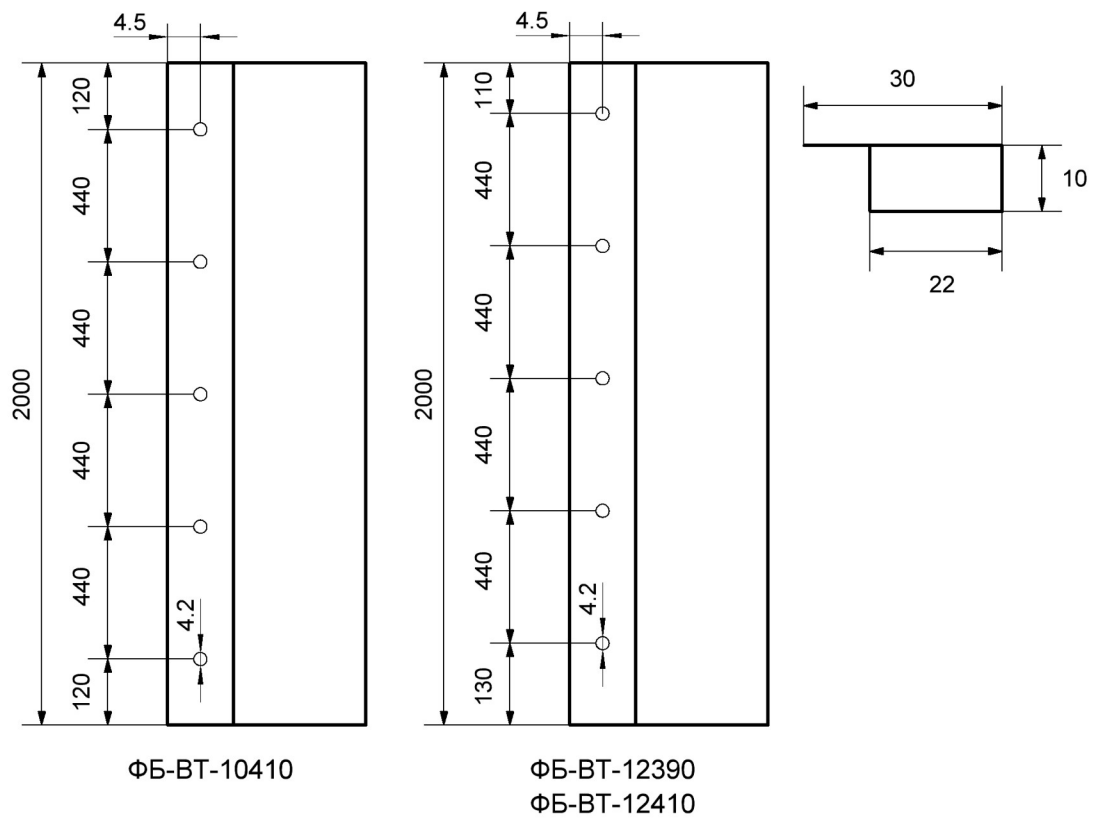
Габаритные размеры фотобарьера (в мм)
